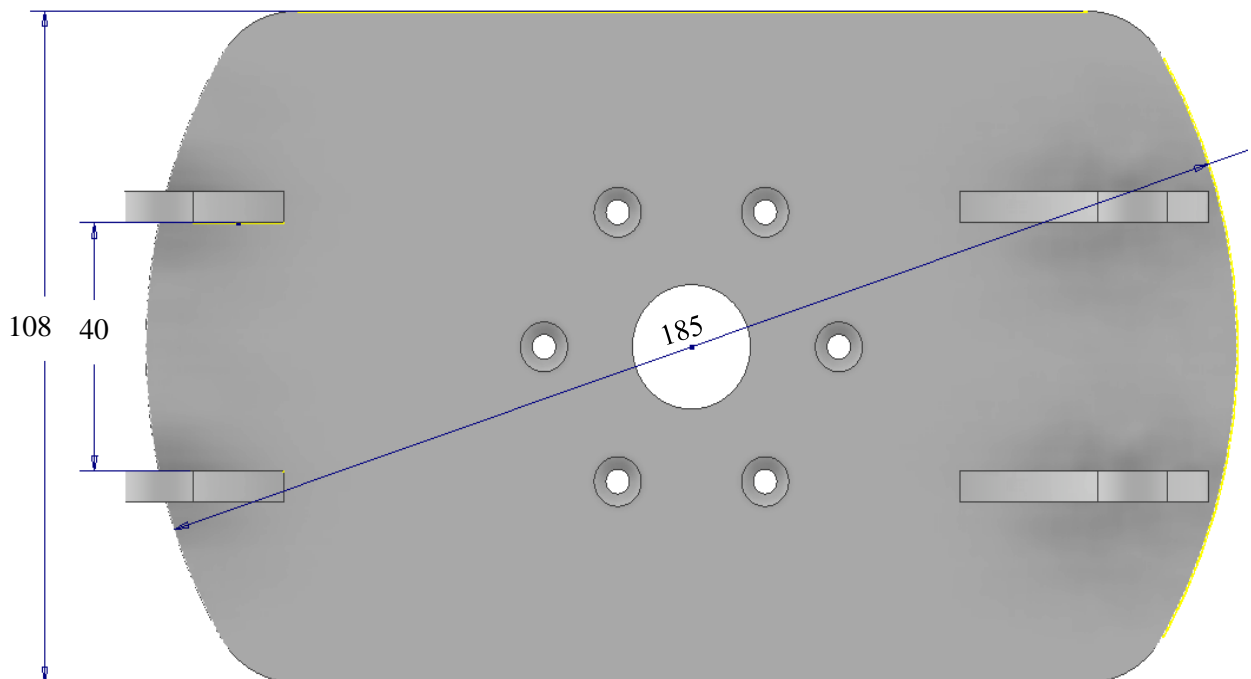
Розміри початкової ланки, вид зверху
